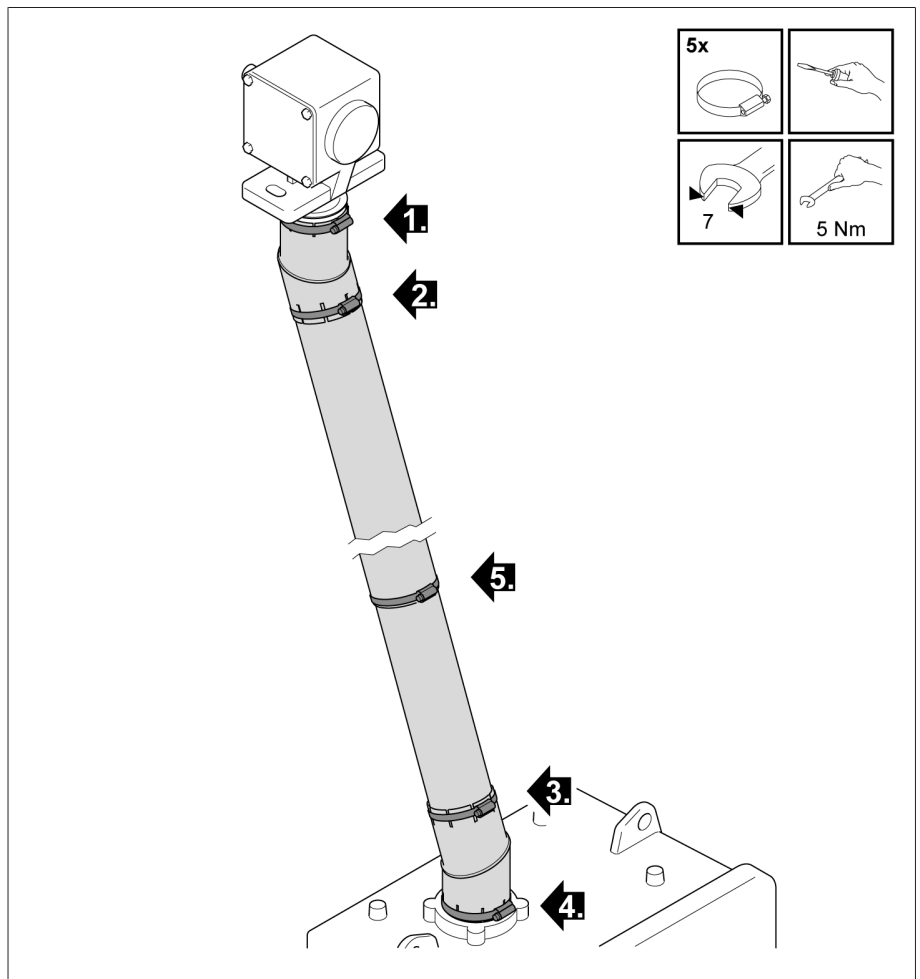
Fixer le tube télescopique protecteur et les tubes de protection rotatifs à l'aide des colliers de serrage
